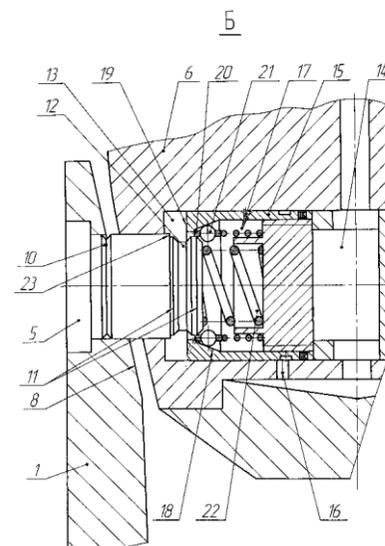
Соединительный узел режущего инструмента с клином и отсоединительным устройством в процессе отсоединения режущего инструмента от клина
